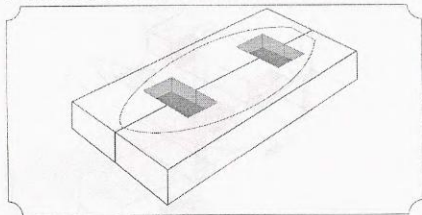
На нижней части заготовки размечают контур корабля в соответствии с чертежом. После этого вырезают пазы под вкладыши
